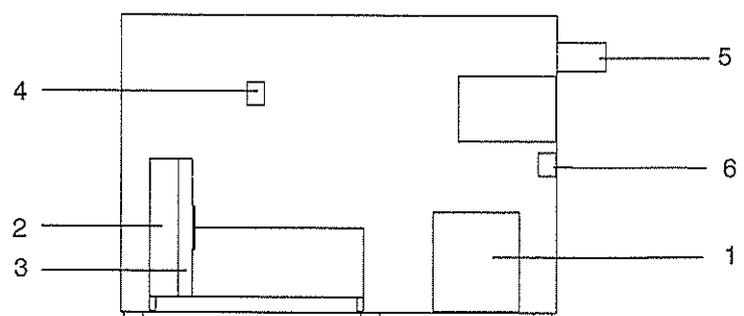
Maschinenteil VMT 04/35 - Seitenansicht
